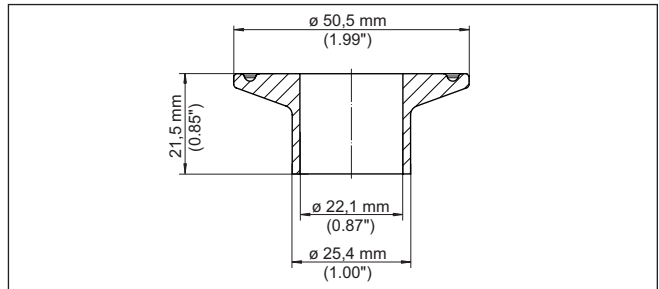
Medidas racor para soldar Clamp 1" (DIN 32676, ISO 2852)
